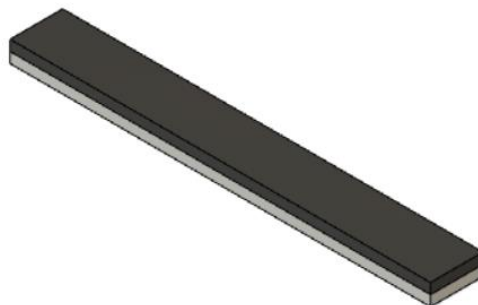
Diseño 3D – Placa bimetálica material acero – aluminio (2020)
